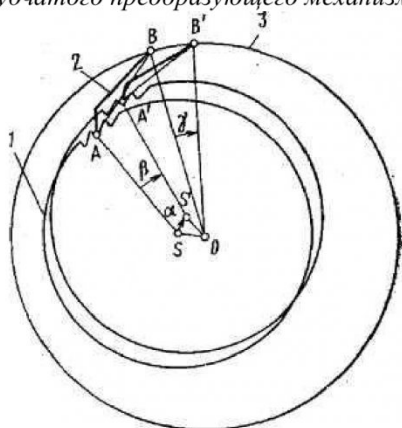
Схема принципа действия выходного зубчатого преобразующего механизма
